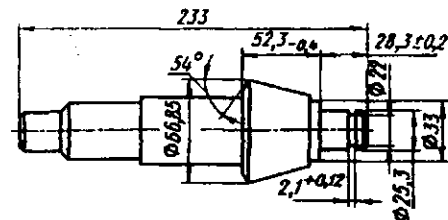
Наладка полуавтомата 116 для обработки одной стороны заготовки ведущего конического зубчатого колеса
